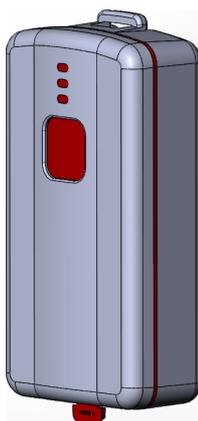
Внешний вид прибора «Юпитер-6422»
